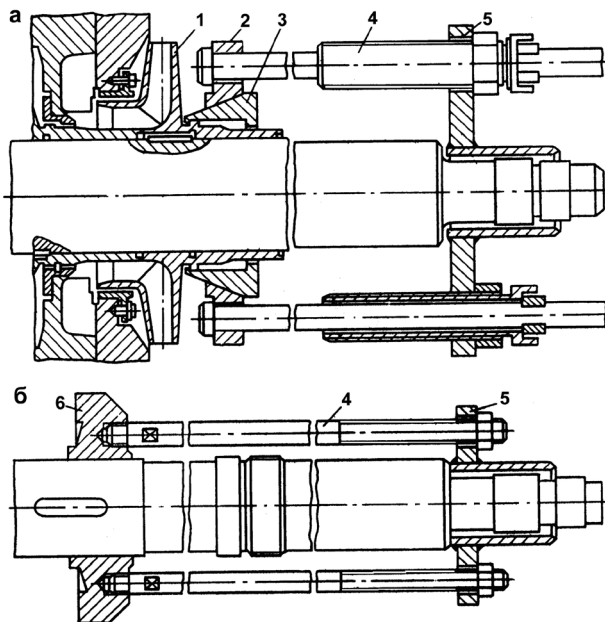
Приспособления для снятия деталей с вала насоса: *a* — для снятия рабочих колес и защитных втулок, *б* — для снятия разгрузочного диска; *1* — рабочее колесо, *2* — кольцо, *3* — захваты, *4* — шпильки, *5* — фланец, *6* — разгрузочный диск
